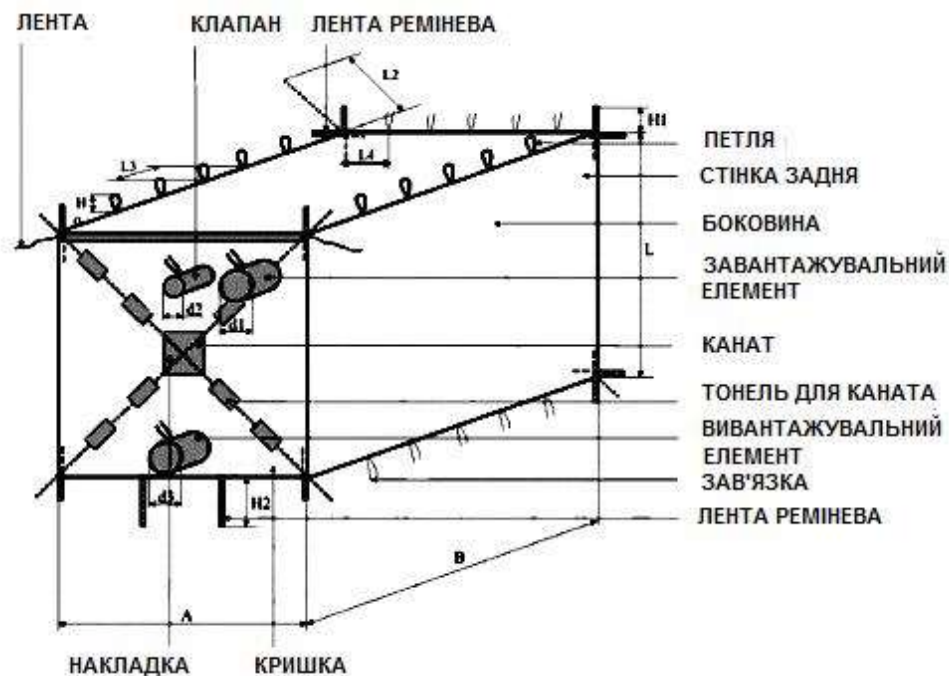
Загальний пристрій контейнерного вкладиша
